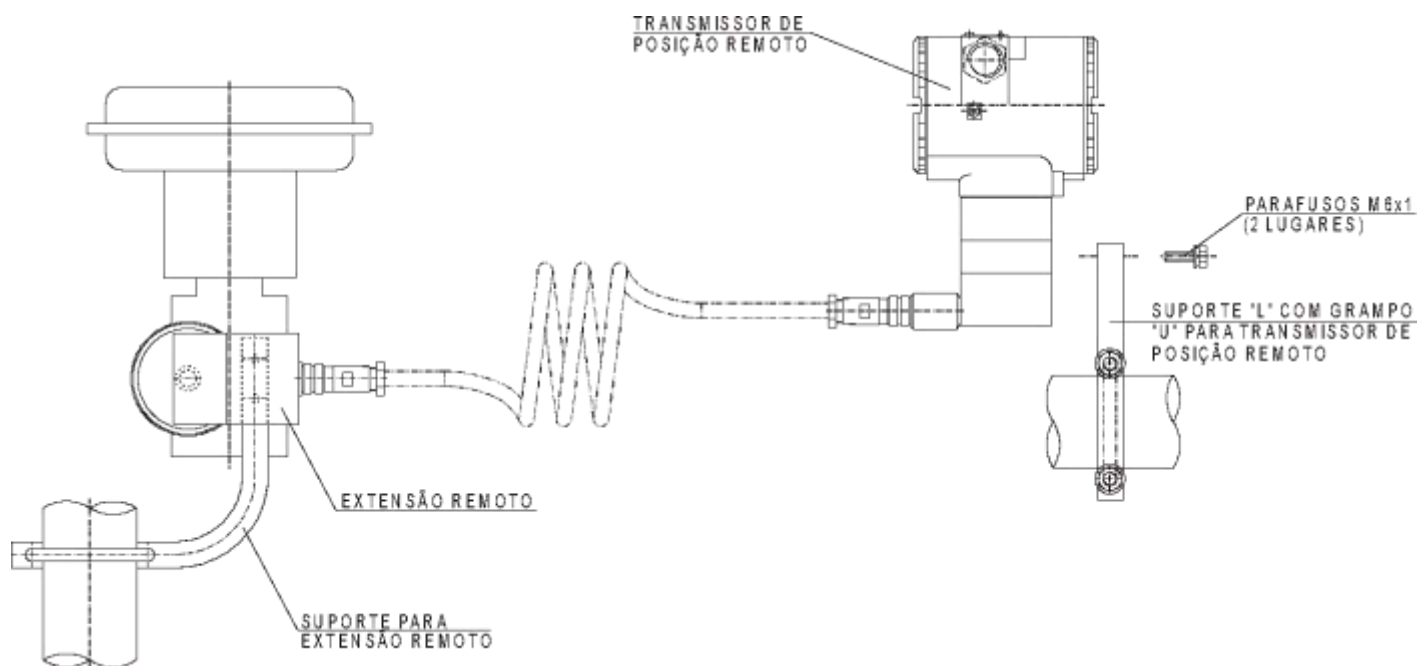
Transmissor de Posição em Atuador Rotativo com Sensor de Posição Remoto
